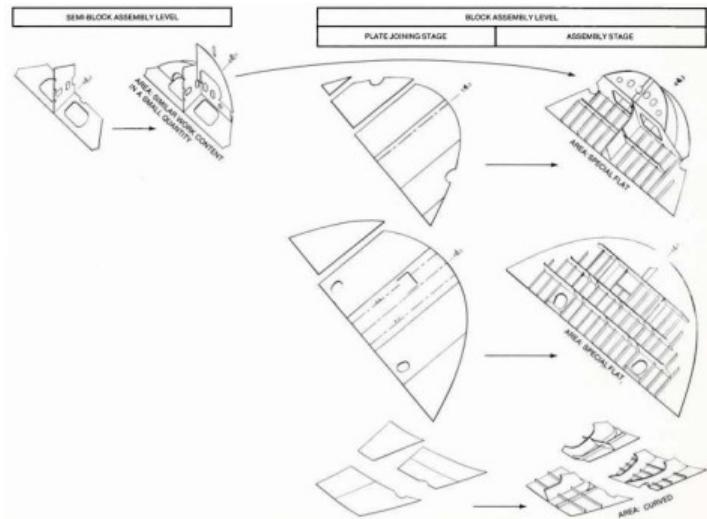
Block Assembly pada Upper Deck and Engine-room Flat
